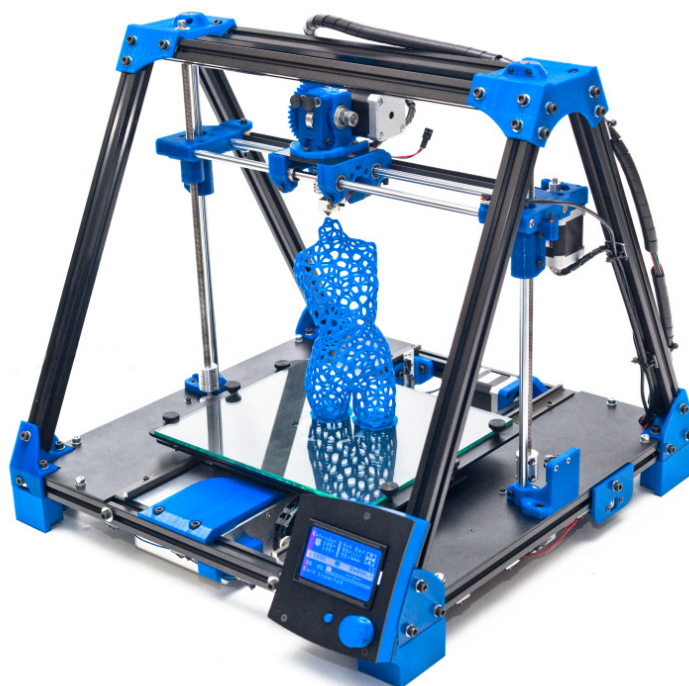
Kit d'Impressió BCN3D+ assemblet.
